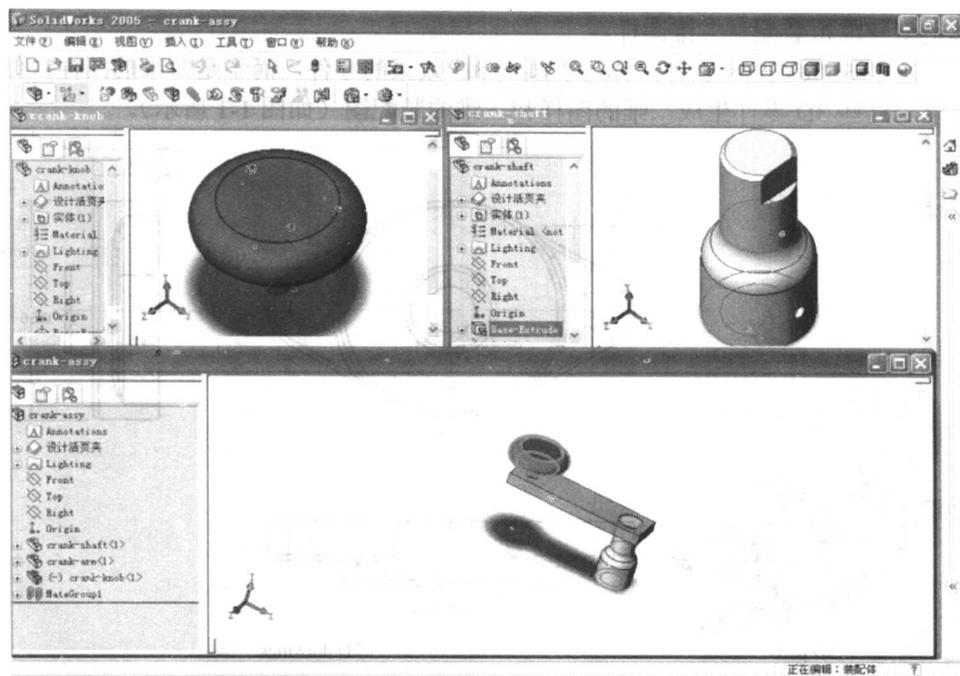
SolidWorks 的三种文件: part、assembly、drawing
